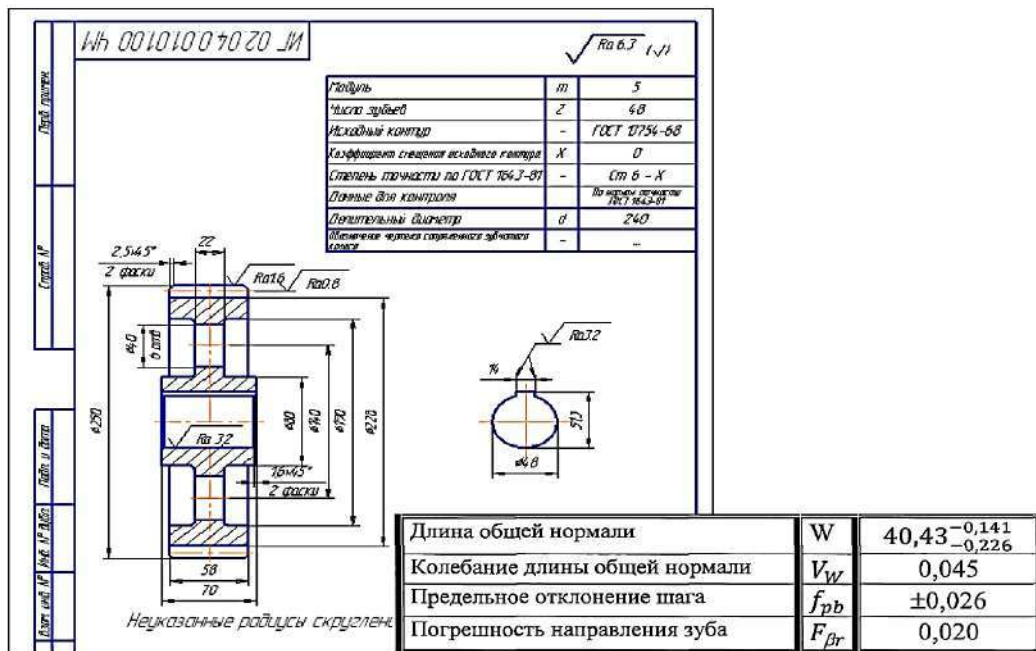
Креслення зубчастого колеса з параметрами контролю
